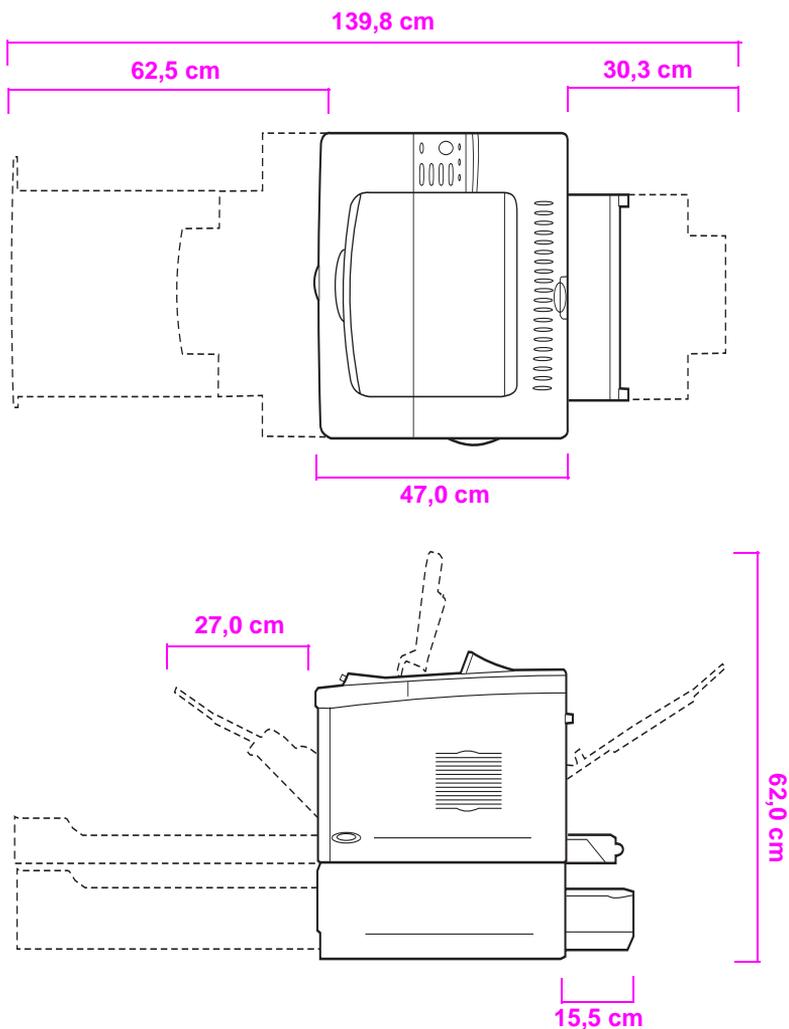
Dimensions des imprimantes HP LaserJet 5000 N et 5000 GN (vues supérieure et latérale)
